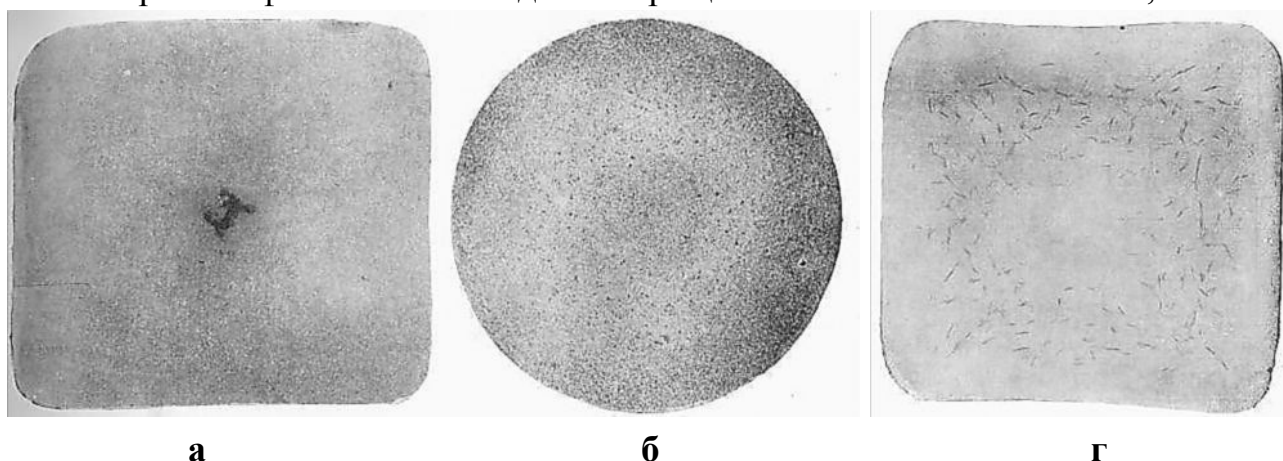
Пороки макроструктуры стали: остатки усадочной раковины (а), общая пористость (б) и флокены (в).
